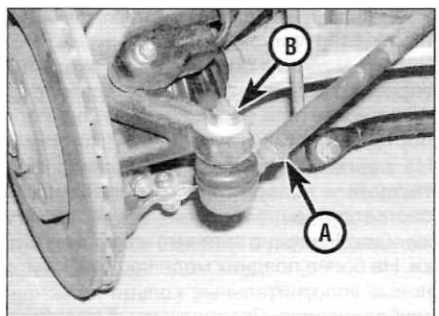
Контргайка шарового шарнира рулевой тяги (А) и гайка крепления шарового шарнира к поворотному кулаку (В)
